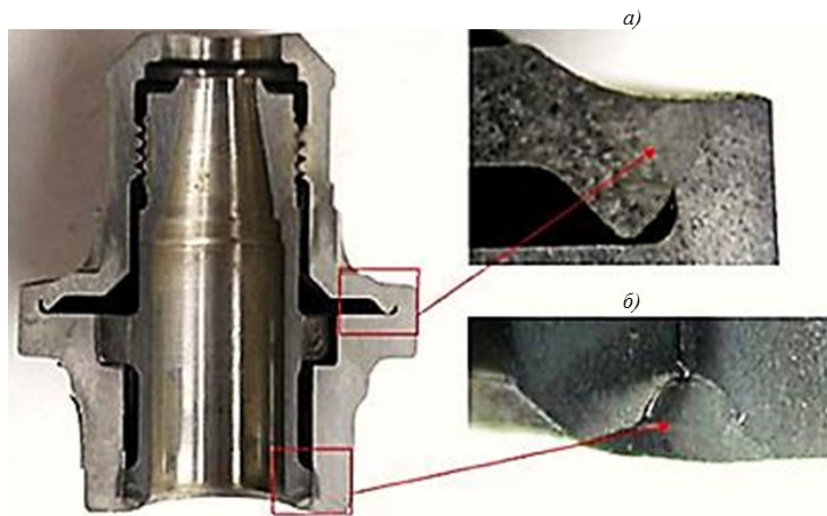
Продольный шлиф сварных швов форсунки 2 (а) и 1 (б)
